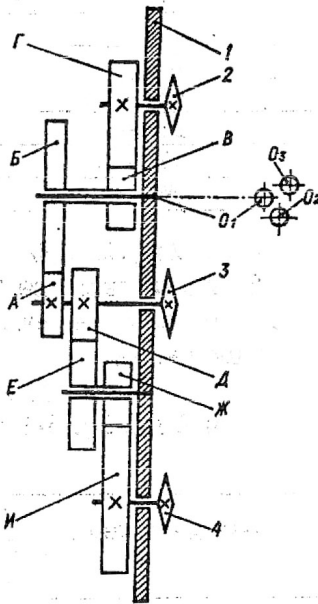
Схема редуктора сеялок типа СЗ-3,6 (СЗ-3,6А) и СЗП-3,6, оборудованных шестеренчатым редуктором, вид сзади:
